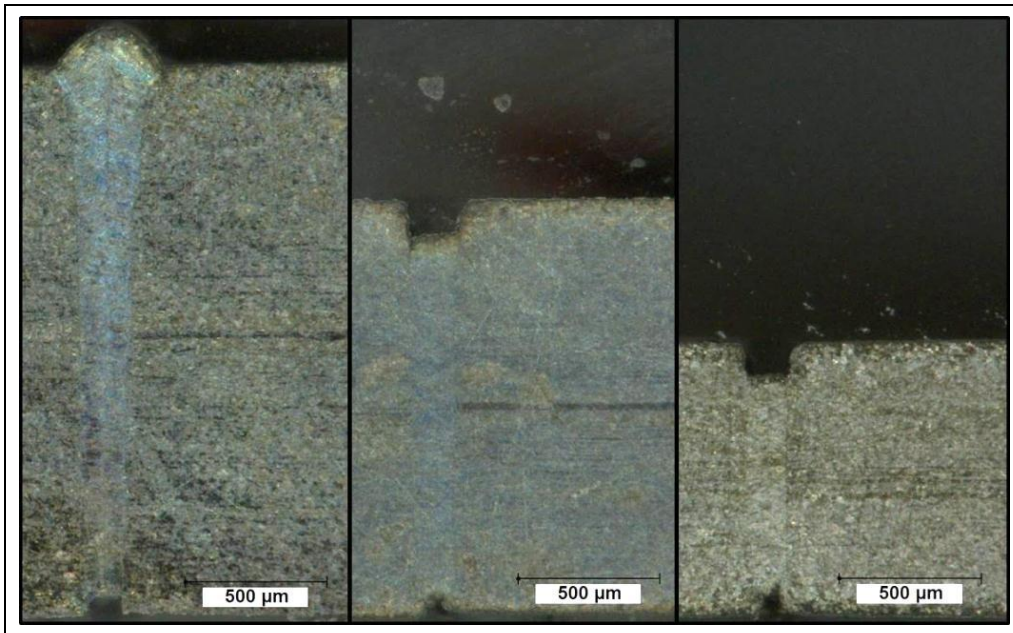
Querschliffaufnahmen der Schweißnähte am X5CrNi18-10
